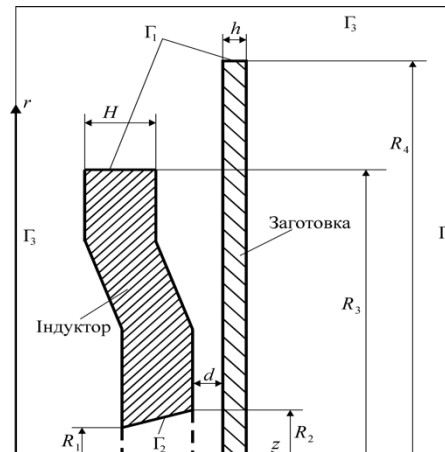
Розрахункова схема розрахункова схема складеного одновиткового індуктора та плоскої заготовки
